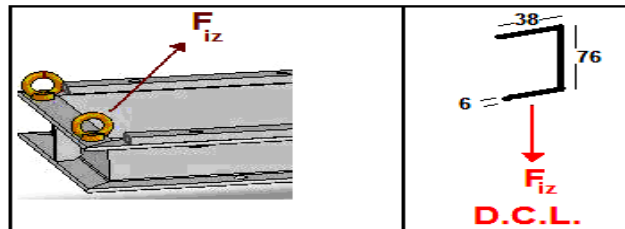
Diagrama de fuerzas actuantes para el cálculo de espesor de soldadura.
